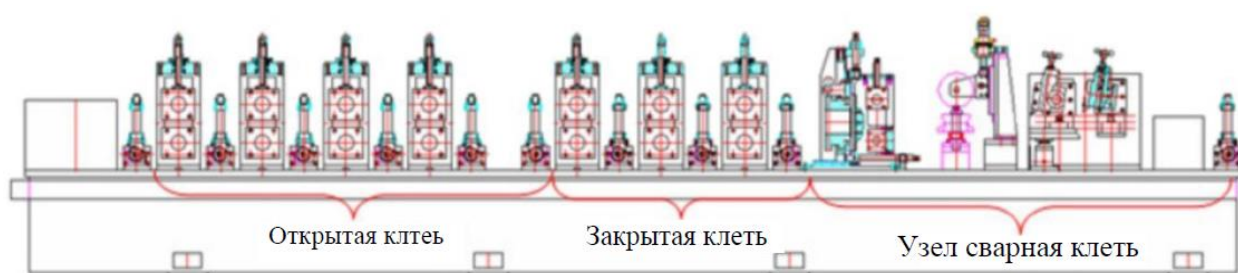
Схема типичного валкового формовочного оборудования при производства сварных труб
